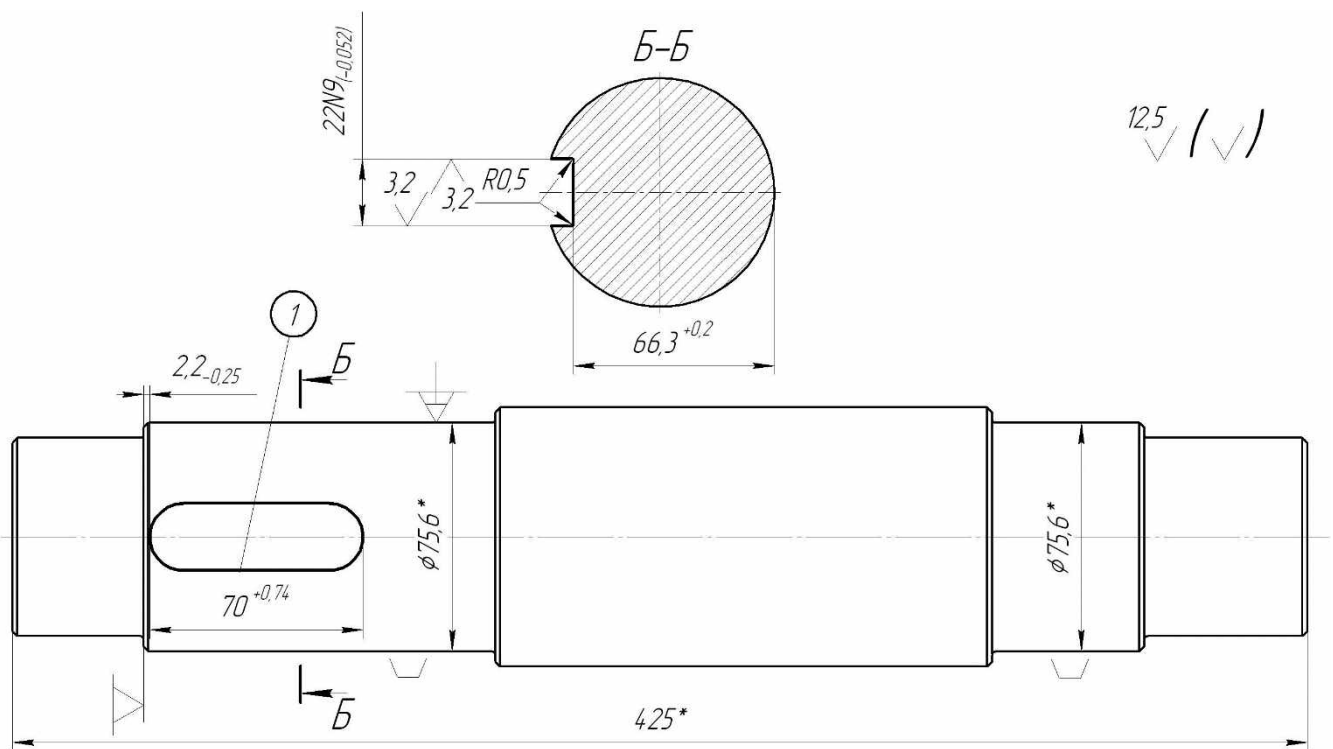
Ескіз оброблення деталі під час, операція 025
